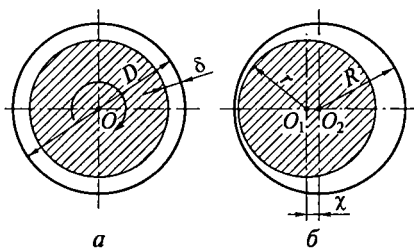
Схема концентричного (а) и эксцентричного (б) зазора плунжерной пары:
